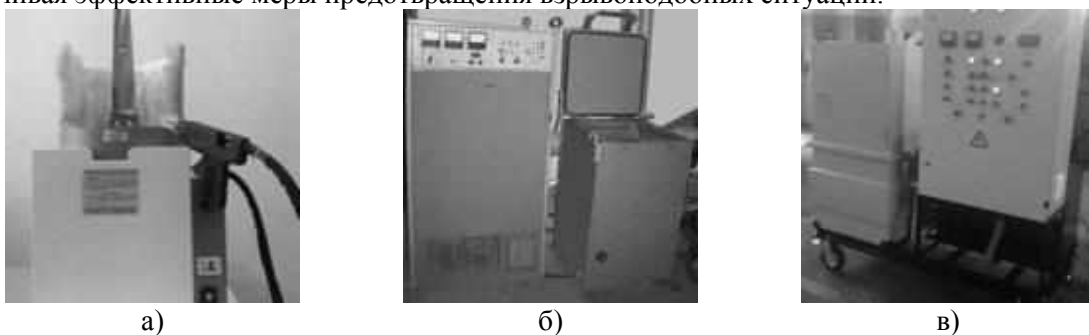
Установка (а) - ЭПП-40; (б) - установка УЗГ-4; (с) - пароструйное устройство УПС 4.3-гейзер
